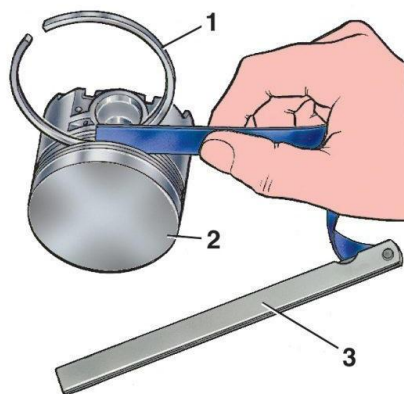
Проверка бокового зазора между кольцом и канавкой поршня: 1 – поршневое кольцо, 2 – поршень, 3 – набор щупов
